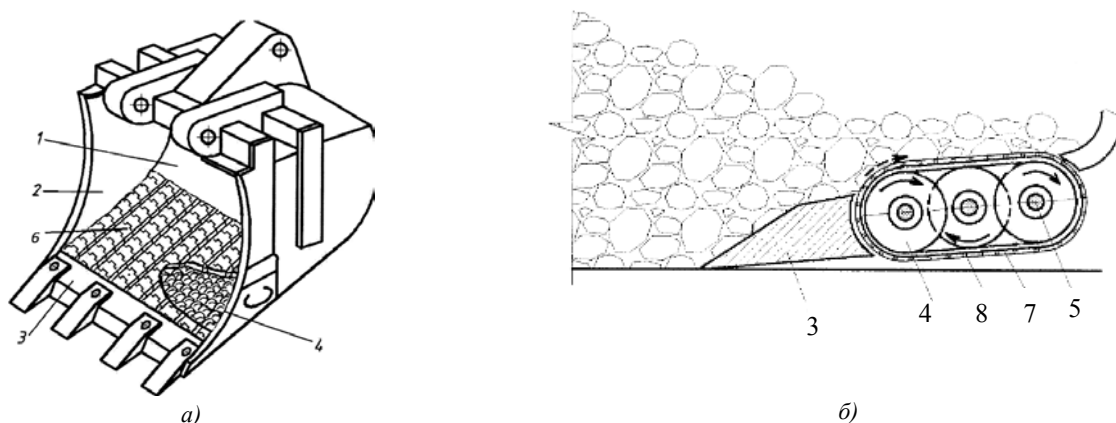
Ковшовый рабочий орган с конвейерным днищем в виде замкнутой ленты (а) и его положение перед штабелем кусковой горной массы (б): 1 — емкость ковша; 2 — боковые стенки; 3 — днище; 4 — ролики; 5 — ось вращения; 6 — лента; 7 — пластины; 8 — пальцы
